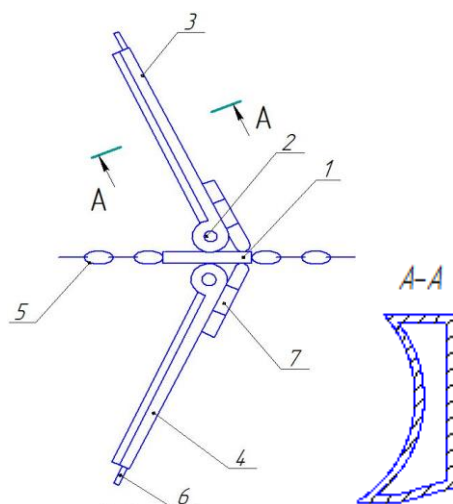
Розроблений скреперний пристрій для прибирання гною.
